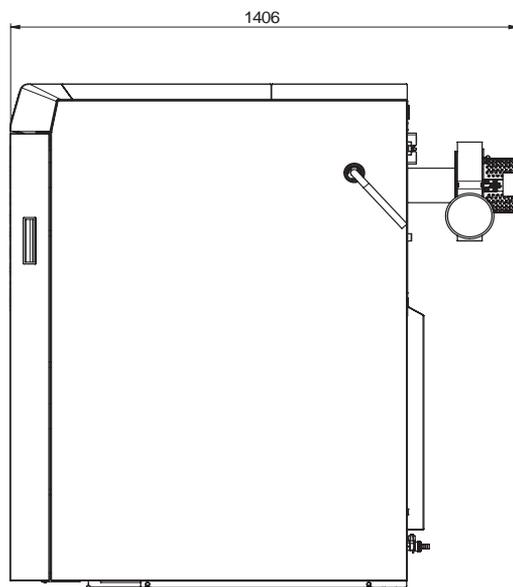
Ventilatore gas combusti con adattatore sulla caldaia – vista da destra
